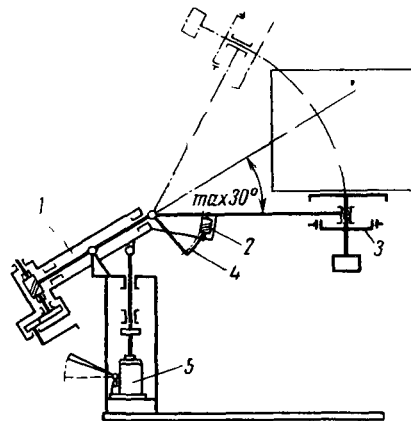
Кинематическая схема универсального установочного манипулятора:
